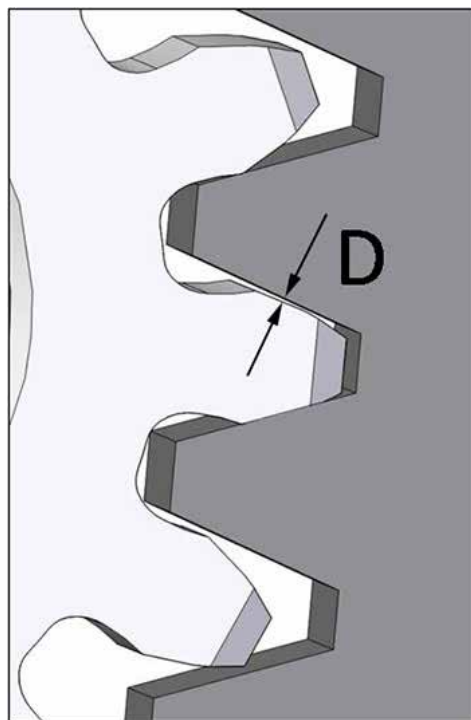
Зазор между зубчатым колесом и зубчатой рейкой.
